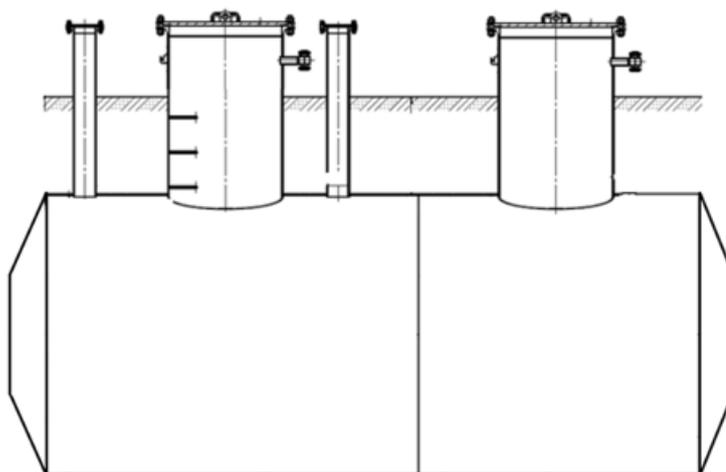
Эскиз резервуаров РГС-12, РГС-16
